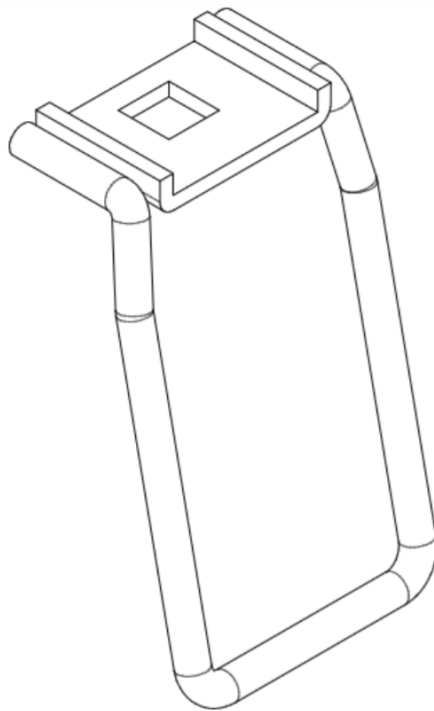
Estribo para braço tipo L (Autor, 2020).
